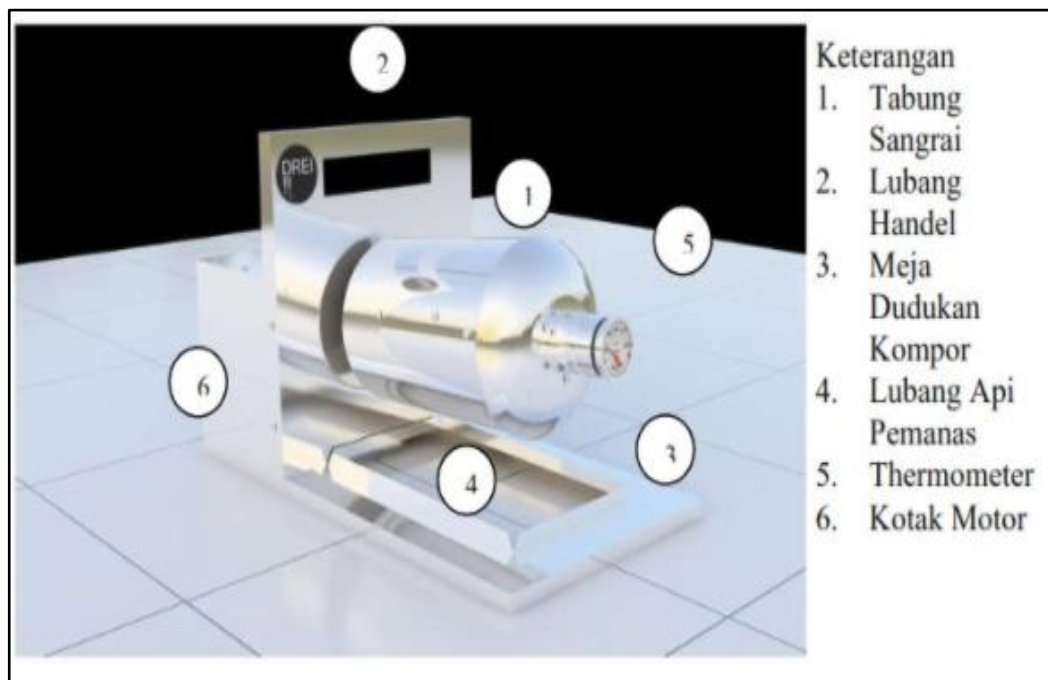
Komponen Komponen Mesin *Roasting
